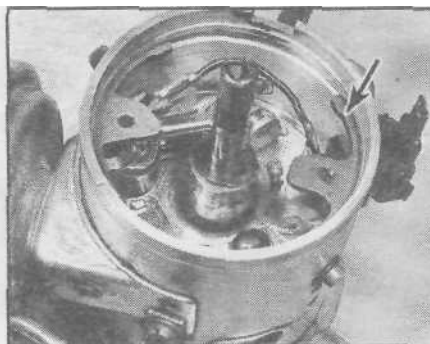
, а. Правильная установка кольца крепления подшипника
